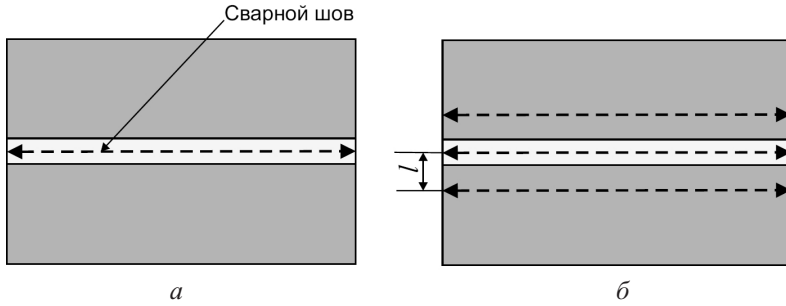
Схемы ЭДО сварных пластин: а – двусторонняя ЭДО сварного шва; б – двусторонняя ЭДО сварного шва и основного металла на расстоянии $l = 20$ и 10 мм от центра шва.
